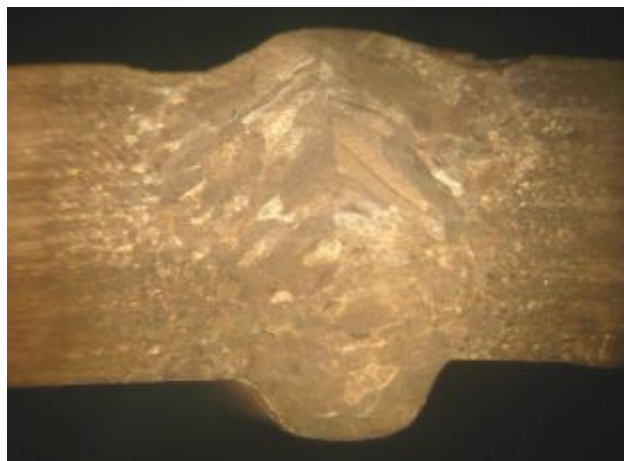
Макрошлиф экваториального сварного шва. Материал VT14C (×5)
